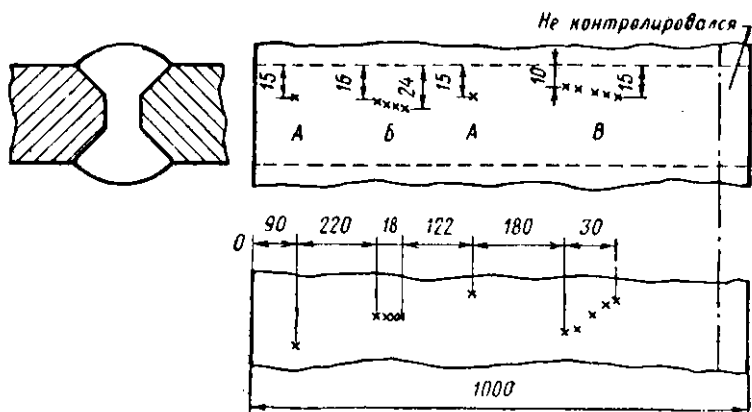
Карта ультразвукового контроля стыкового сварного шва (по ГОСТ 14782—69)
